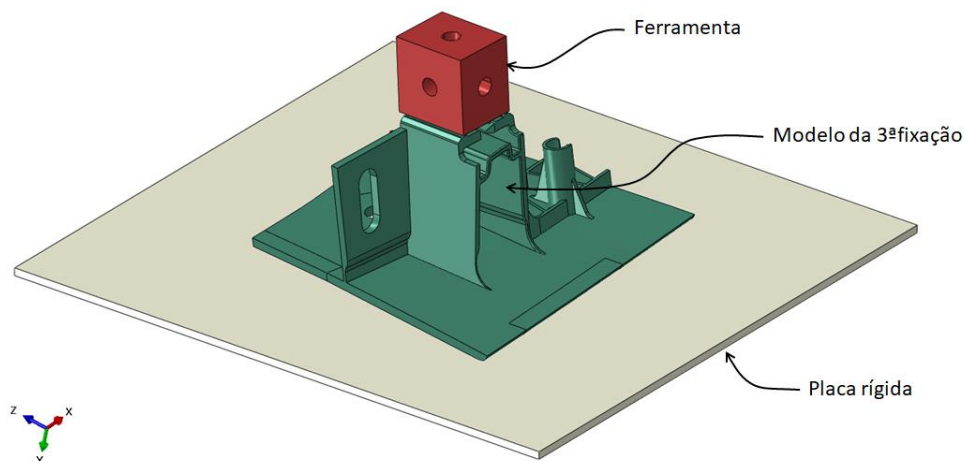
Montagem do conjunto da 3ª fixação no módulo “*Assembly*” do Abaqus.
